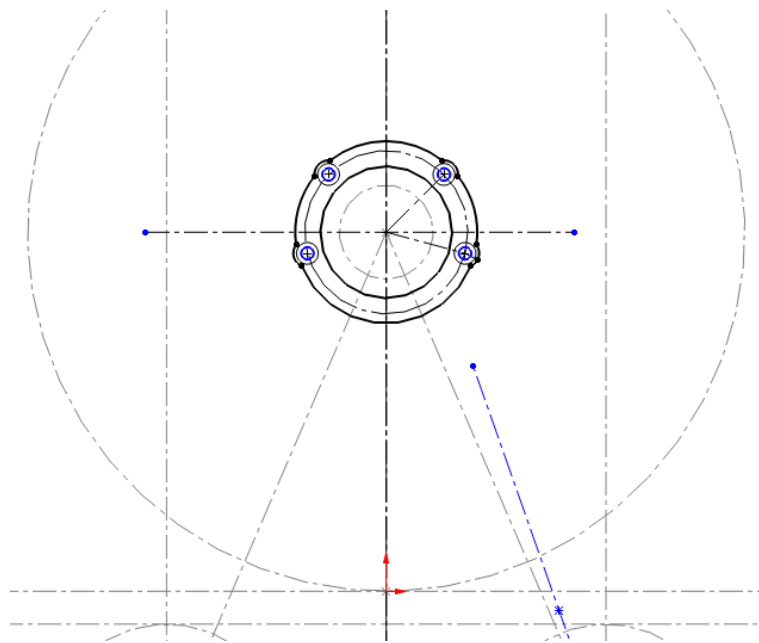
Diseño de la parte superior de la pieza asiento de rodamiento
